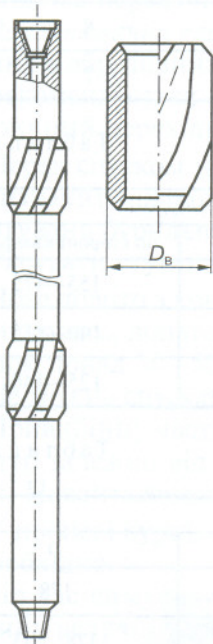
Схема ОБТ із приварними протиприхватними сталевими втулками
